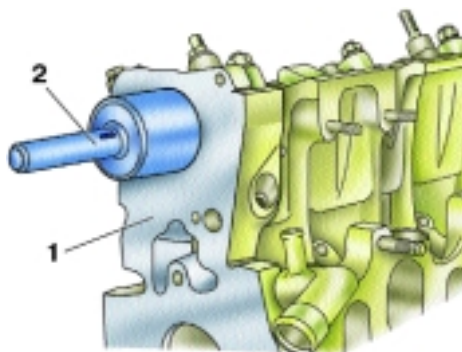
Установка оправки для запрессовки заднего сальника распределительного вала на снятой головке блока двигателя F3R 272: 1 – головка блока цилиндров; 2 – оправка
